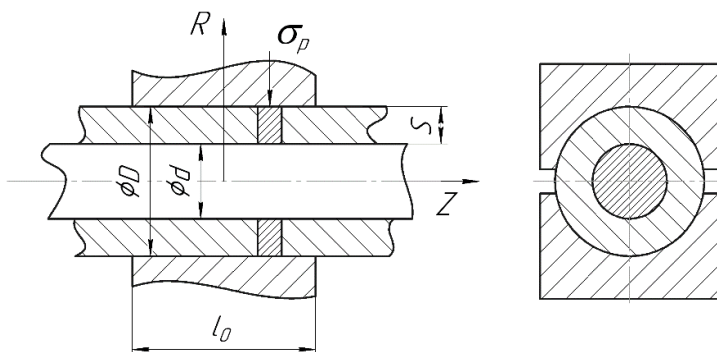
Схема протяжки цилиндрической заготовки в резных бойках с оправкой
